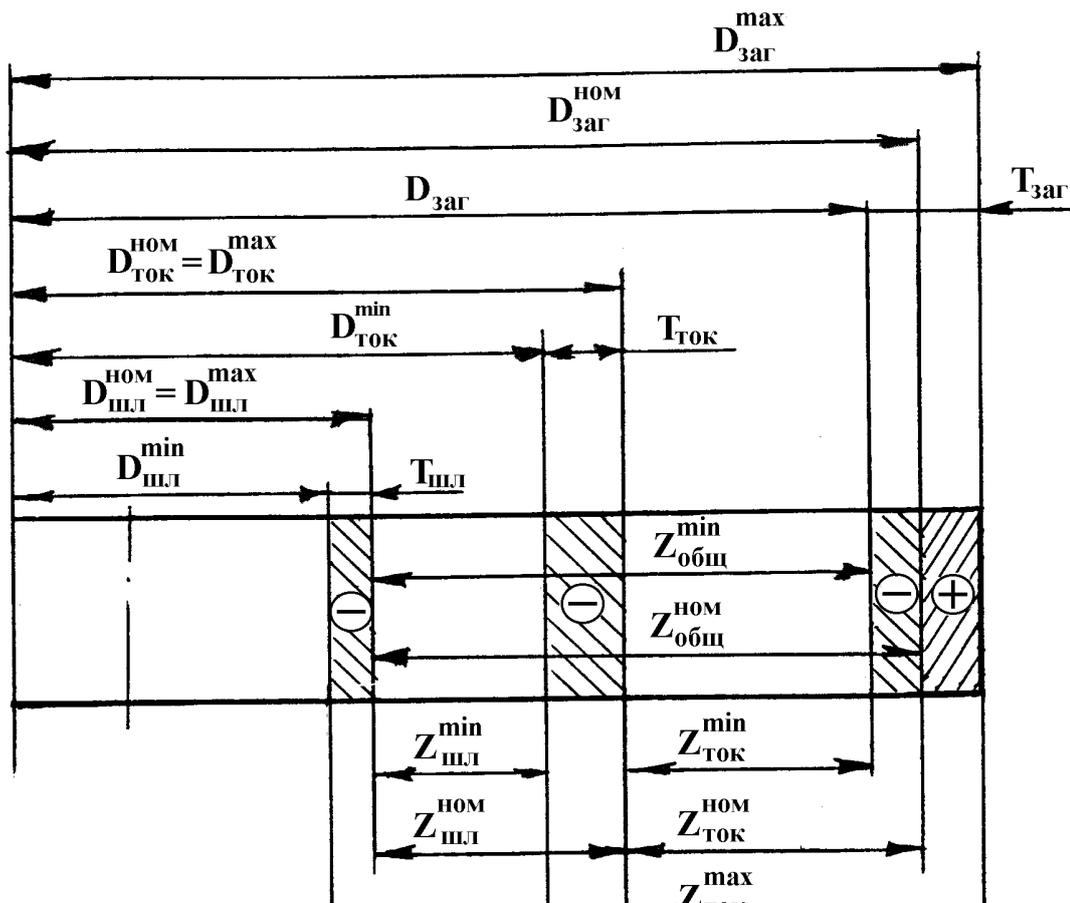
Схема расположения операционных размеров и припусков при обработке цилиндрической поверхности
